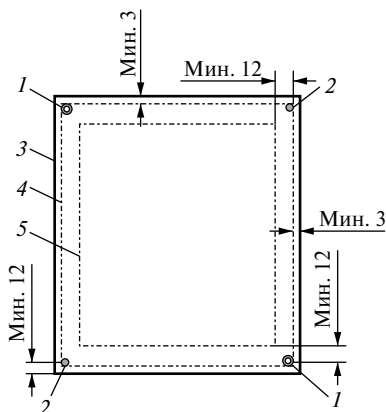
Размещение реперных знаков на заготовке ПП: 1 – базовые отверстия; 2 – реперные знаки; 3 – периметр заготовки ПП; 4 – периметр мультиплицированной заготовки (панели), поступающей на сборку; 5 – рабочее поле заготовки, на котором размещаются платы
